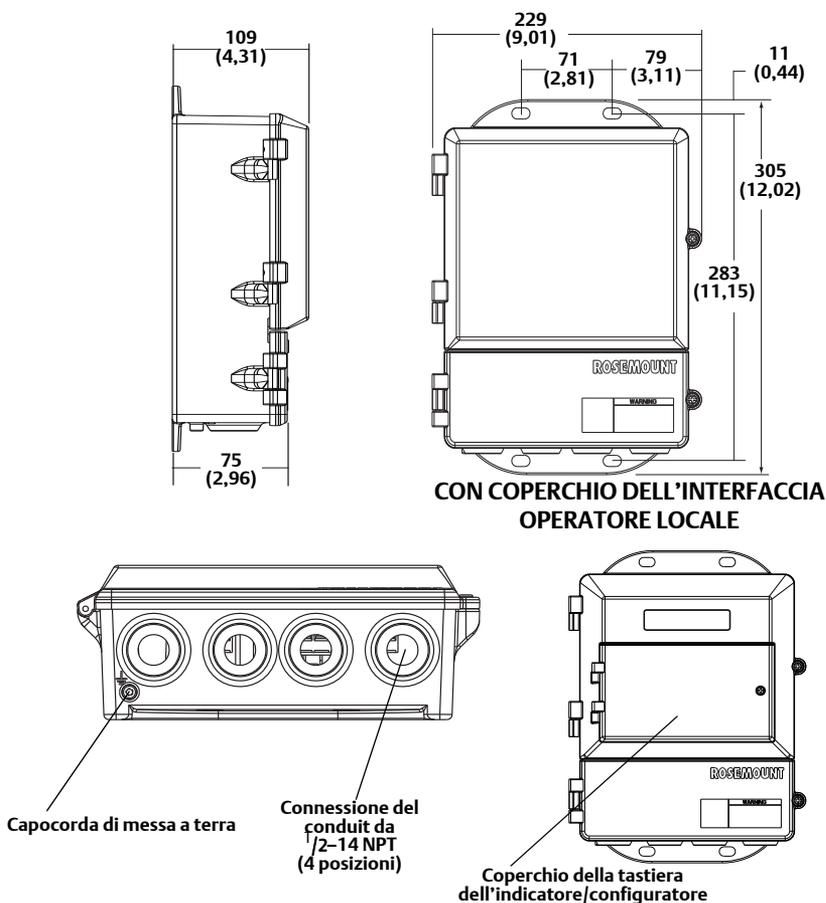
Schema dimensionale del trasmettitore per montaggio sul campo
